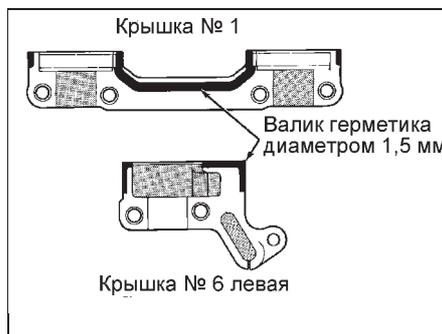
Уплотнение крышки подшипника распределительного вала.
